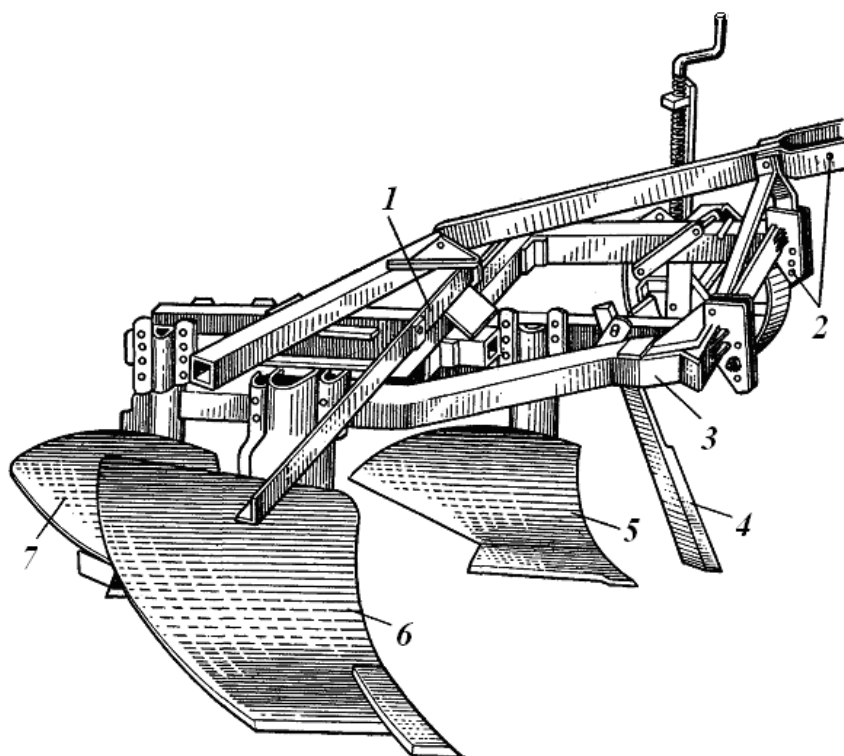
Плуг триярусний начіпний ПТН-40: 1 - причіп для борін; 2 - начіпний пристрій; 3 - рама; 4 - чересловий ніж; 5 - передній корпус; 6 - середній корпус; 7 - задній корпус
